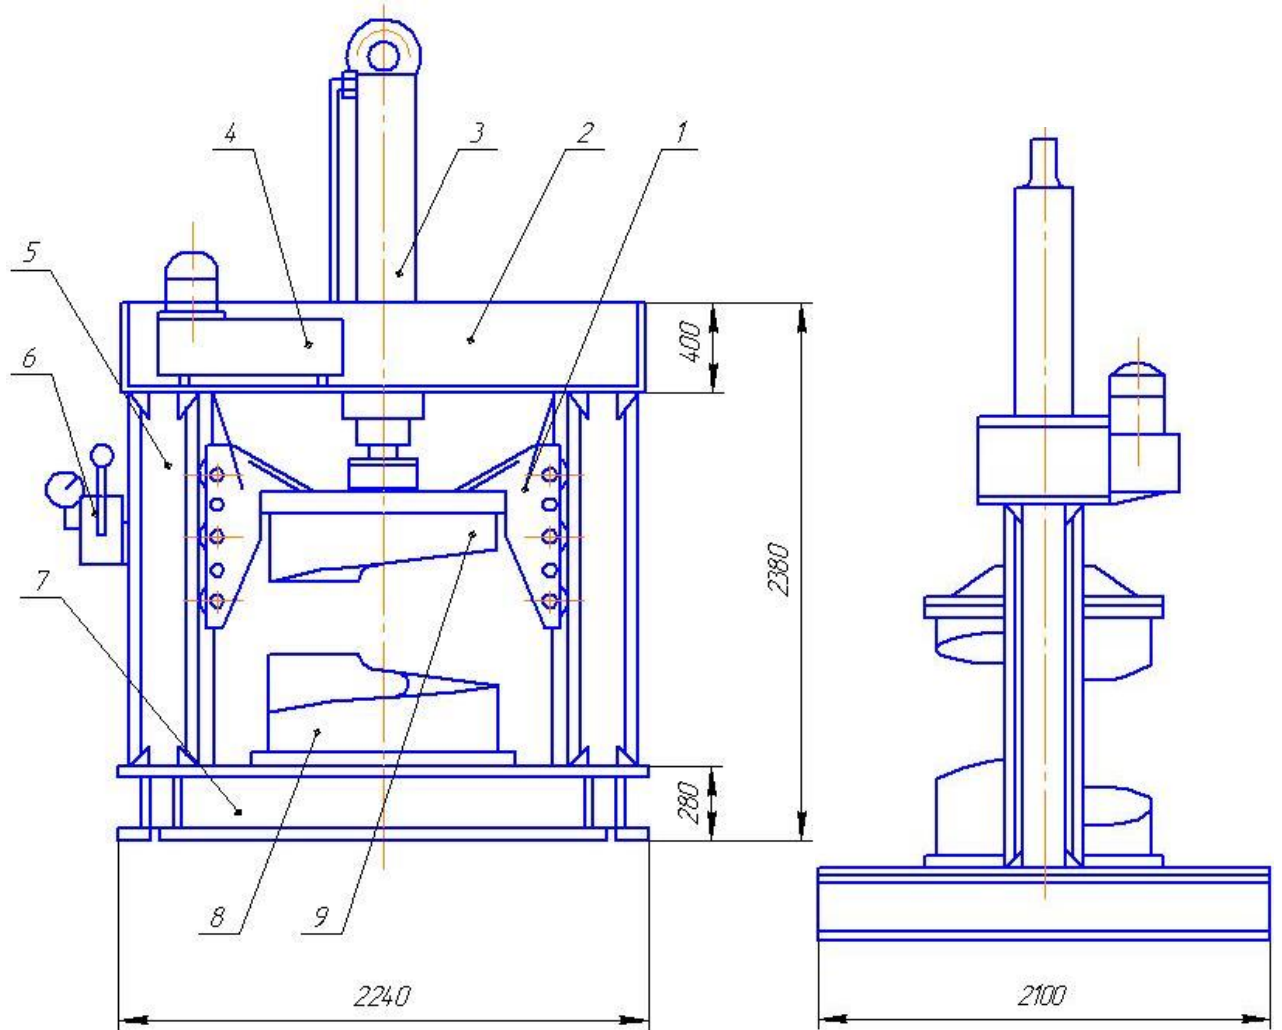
Загальний вигляд преса 001Е із встановленому на ньому штампом: 1 - направляючі салазки; 2 - упорна балка; 3 - гідравлічний циліндр; 4 - насосна станція; 5 - направляючі стійки; 6 - блок керування; 7 - рама; 8 - матриця; 9 - пуансон; 10 - опорна плита, 11 – манометр
